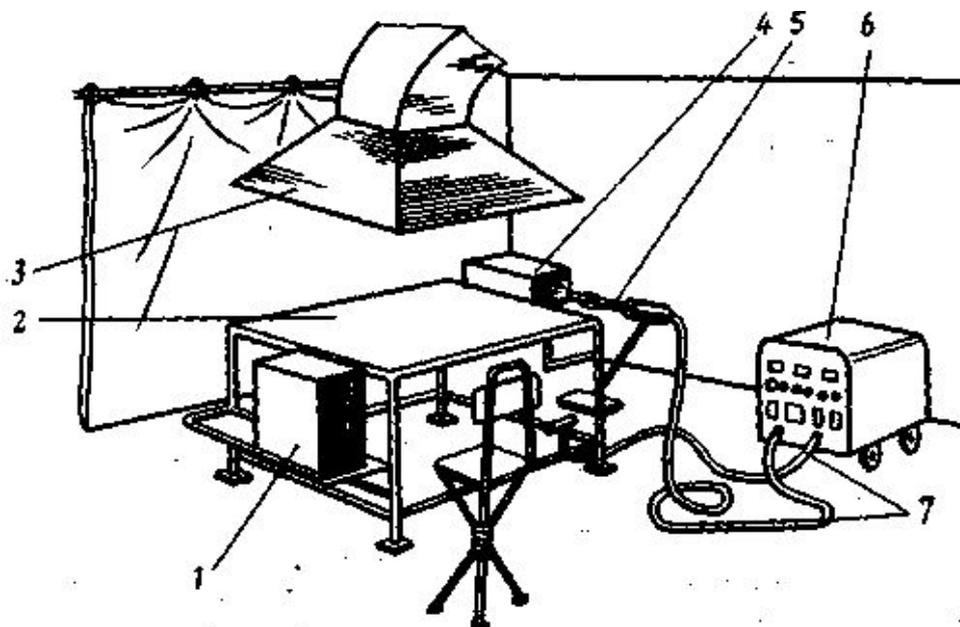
Сварочный пост для ручной дуговой сварки:
